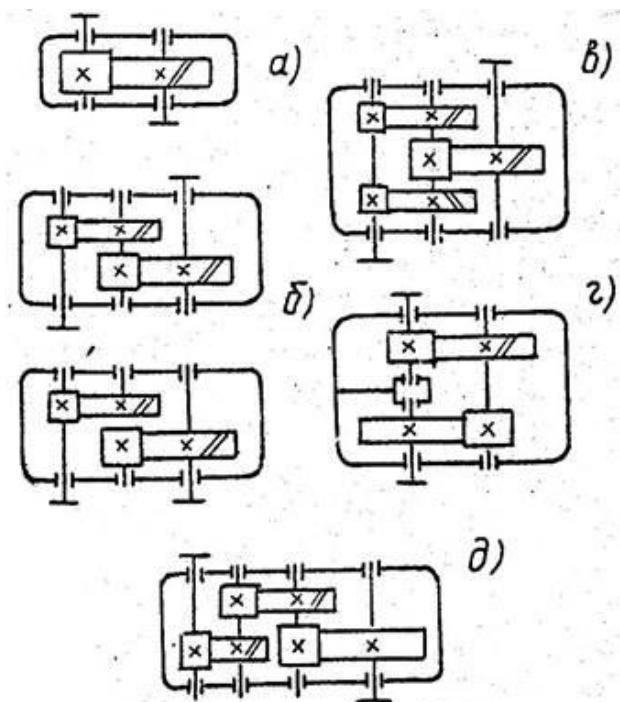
Кинематические схемы зубчатых редукторов
